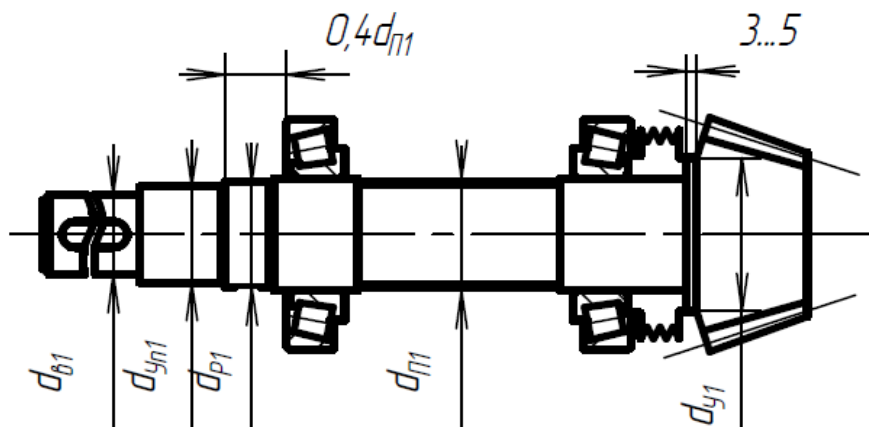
Типова конструкція швидкохідного валу конічного редуктора
